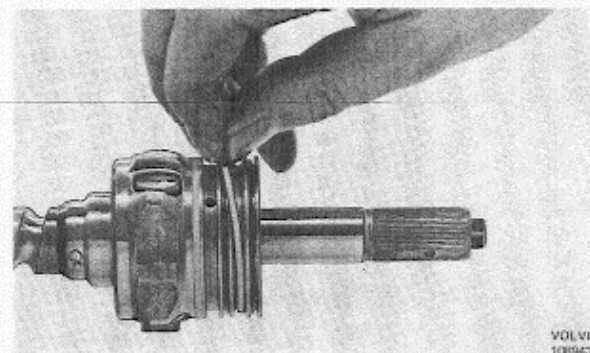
Einbau von O-Ringen und Dichtringen auf dem Schneckenkopf
